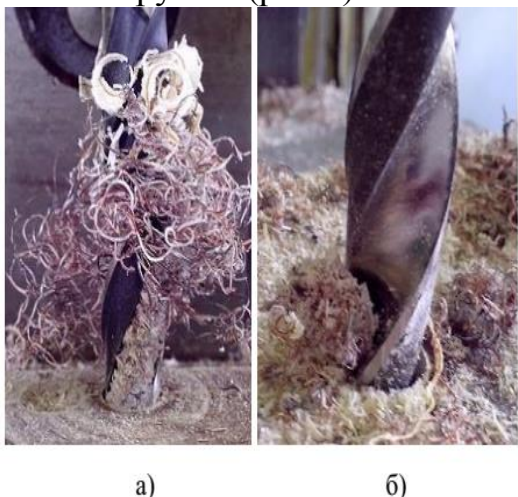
Стружкообразование. а- существующий способ сверления, б- предлагаемый способ сверления
